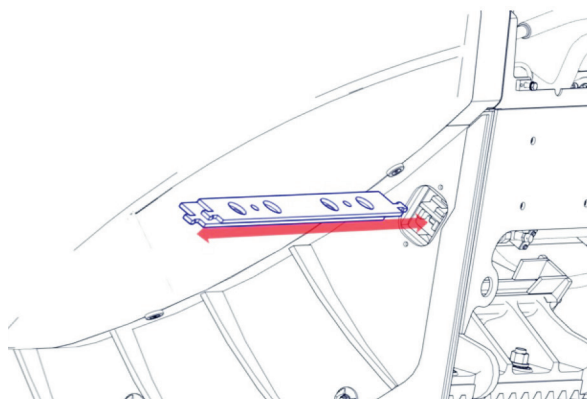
Регулировка зазора: открыть пружинный колпак. Снять два защитных винта М10 и фиксатор пружины.
